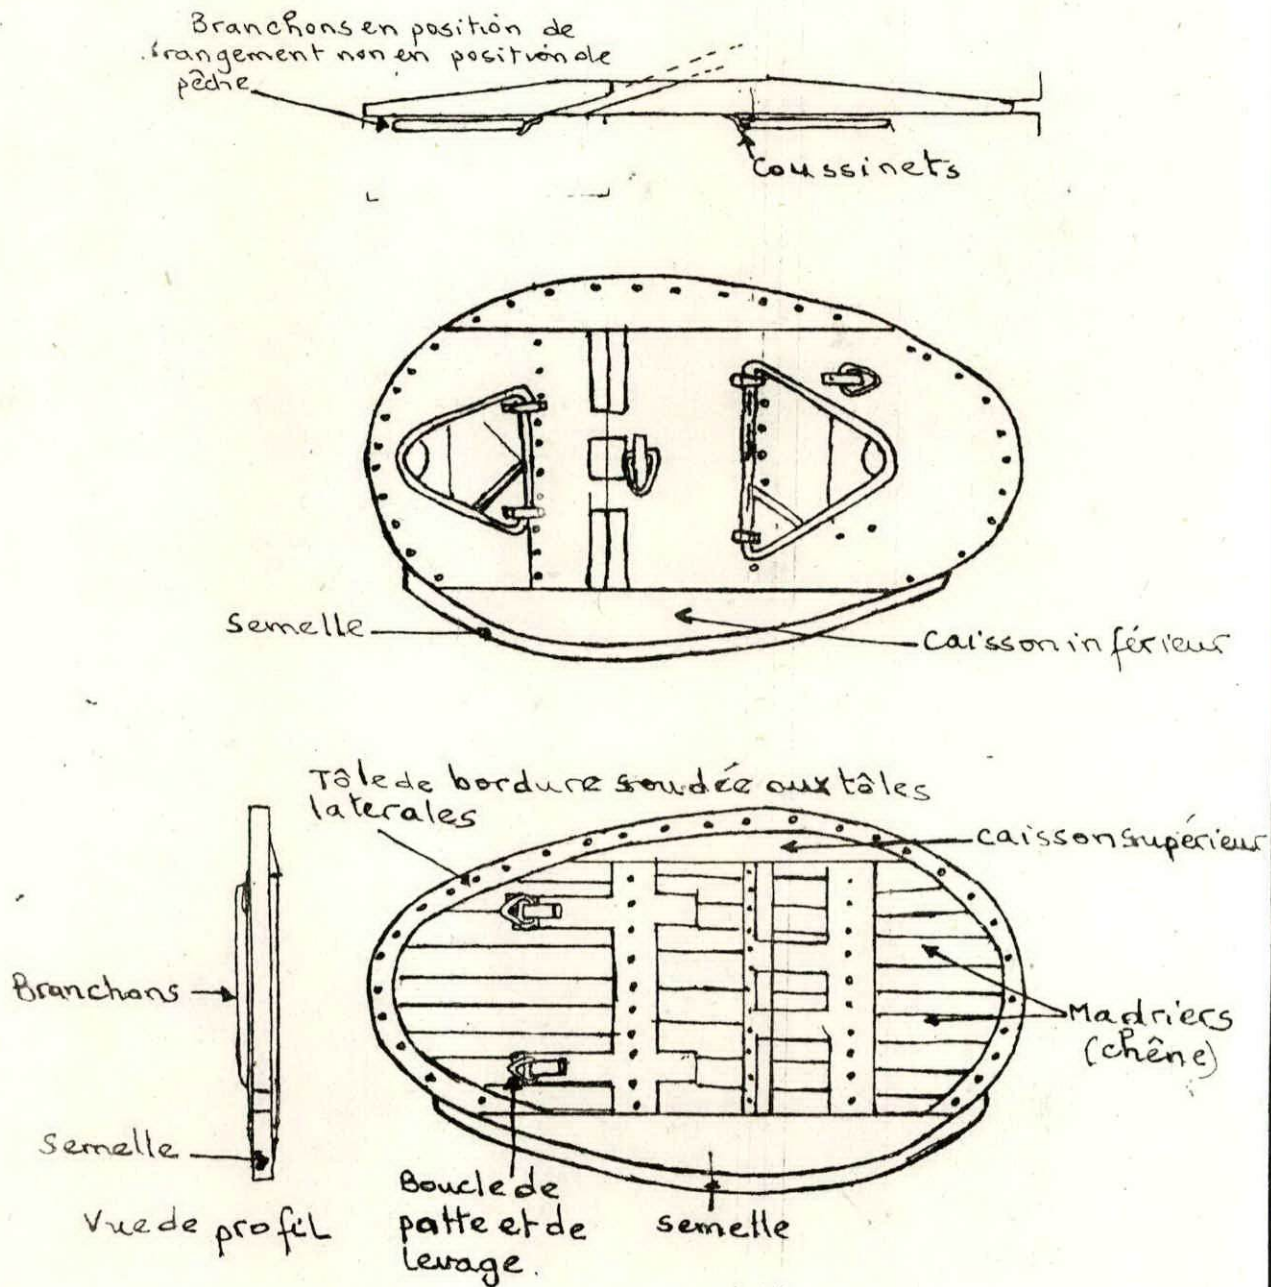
Plan d'un panneau ovale plat avec fente environ, 5.2 m² (F.A.O, 1974).
